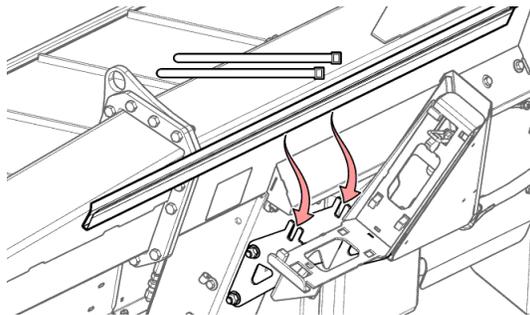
Защитный кожух ножа вертикальных ножниц
